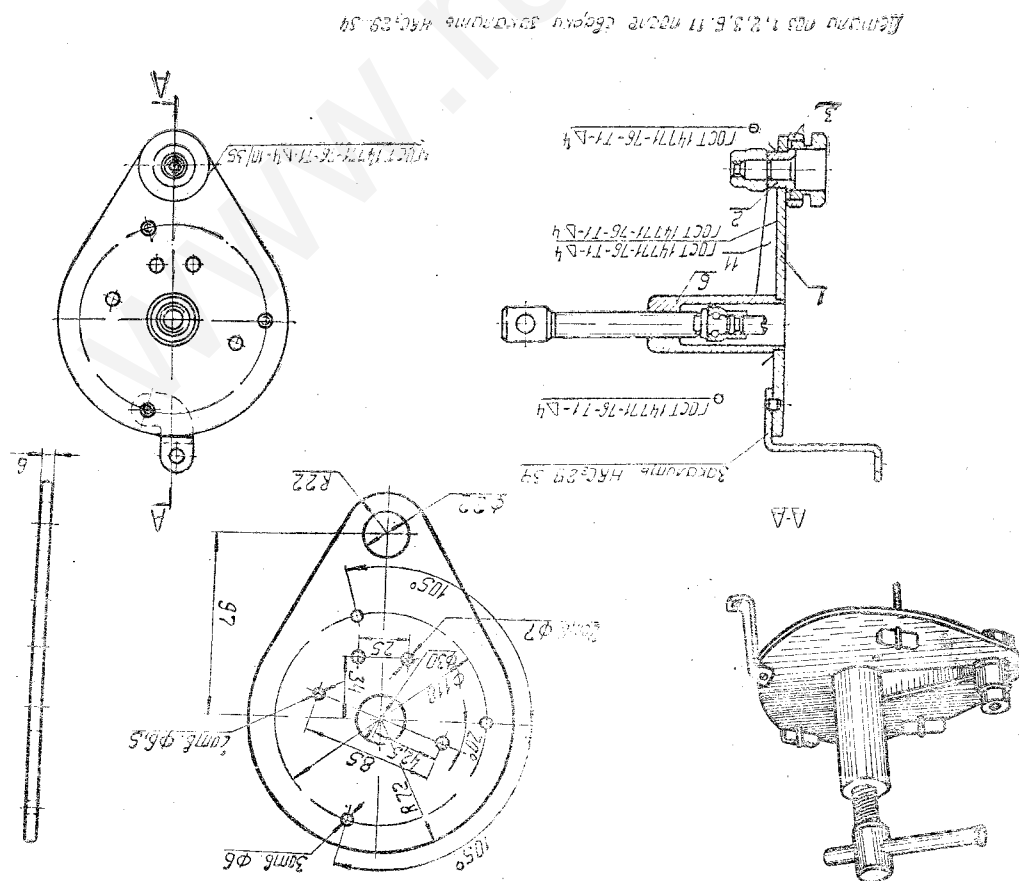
Приспособление для распрессовки и запрессовки коленчатого вала разъединения половин картера
